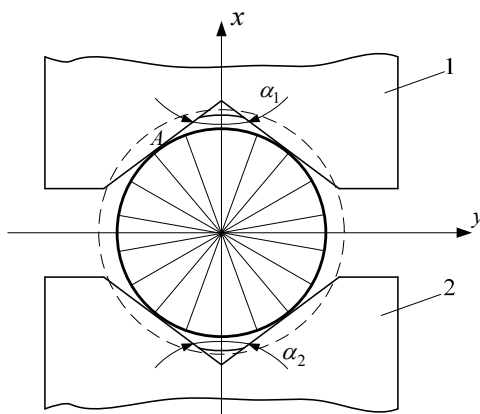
Схема кування заготовки вирізними ромбічними бойками
